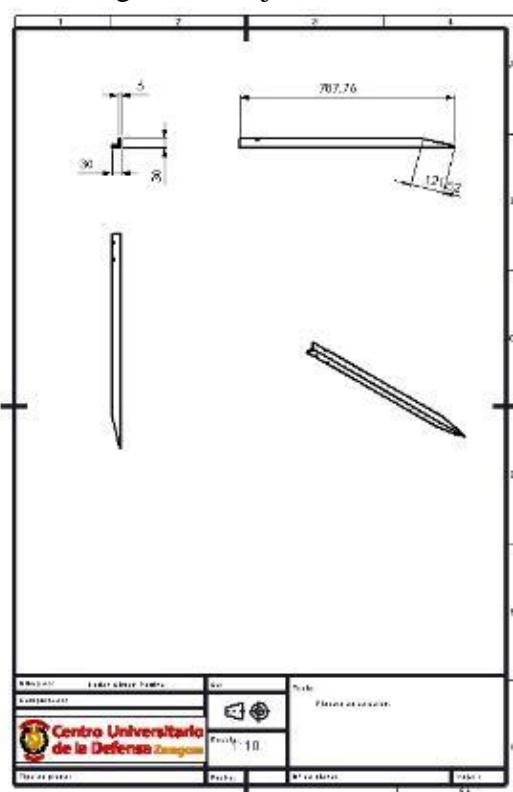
Planos del diseño de la piqueta usada en el implemento.
